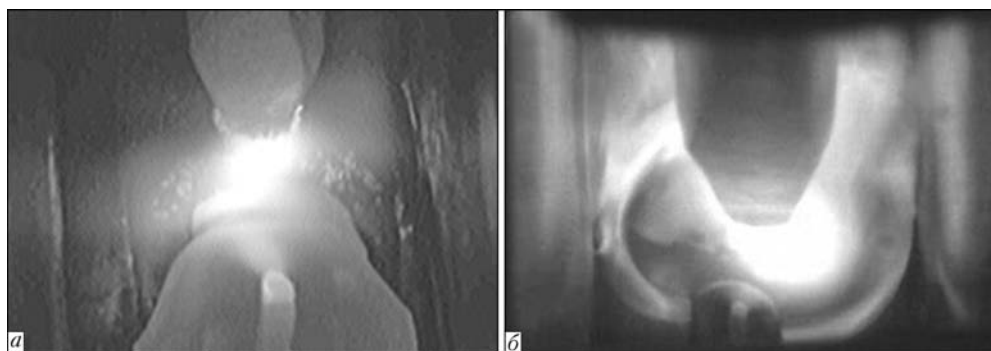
Примеры формируемых изображений зоны сварки ТИГ при токе сварки 100 (а) и 500 (б) А
